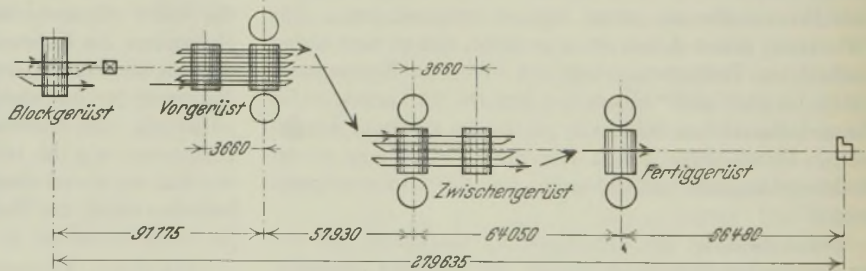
Stichfolge in den Walzgerüsten für Parallelflanschträger.
